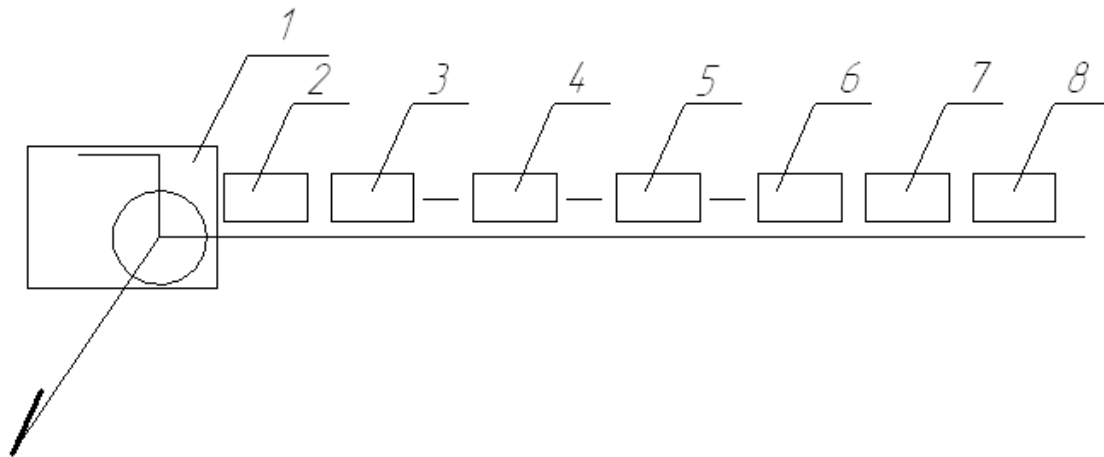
Схема условного обозначения стандартных сварных швов
